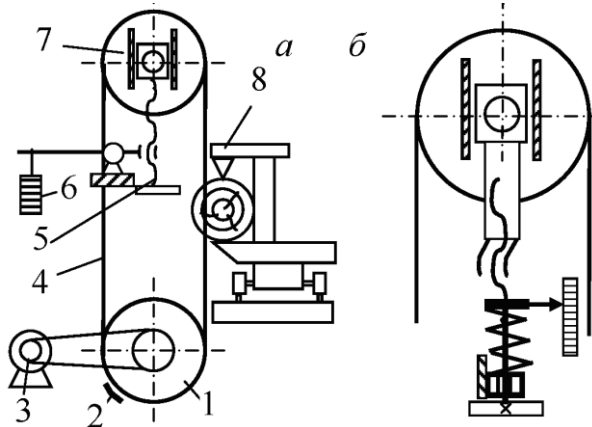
Механізми головного руху стрічкопильних верстатів з натягом пильної стрічки: а - вантажем; б - пружиною
